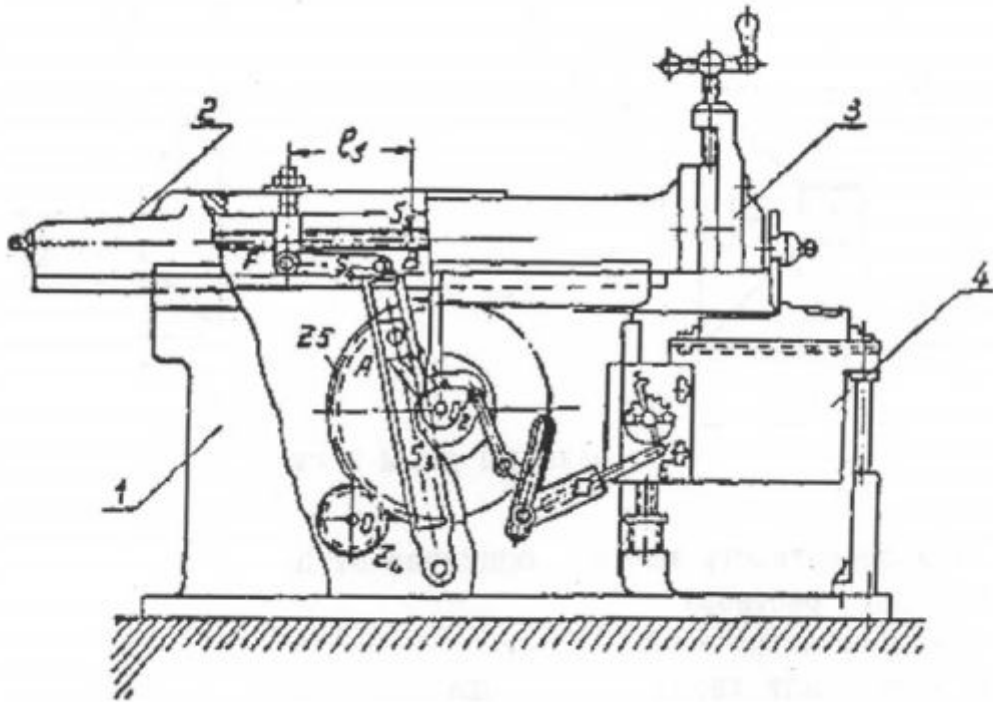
Общий вид поперечно-строгального станка с качающейся кулисой
